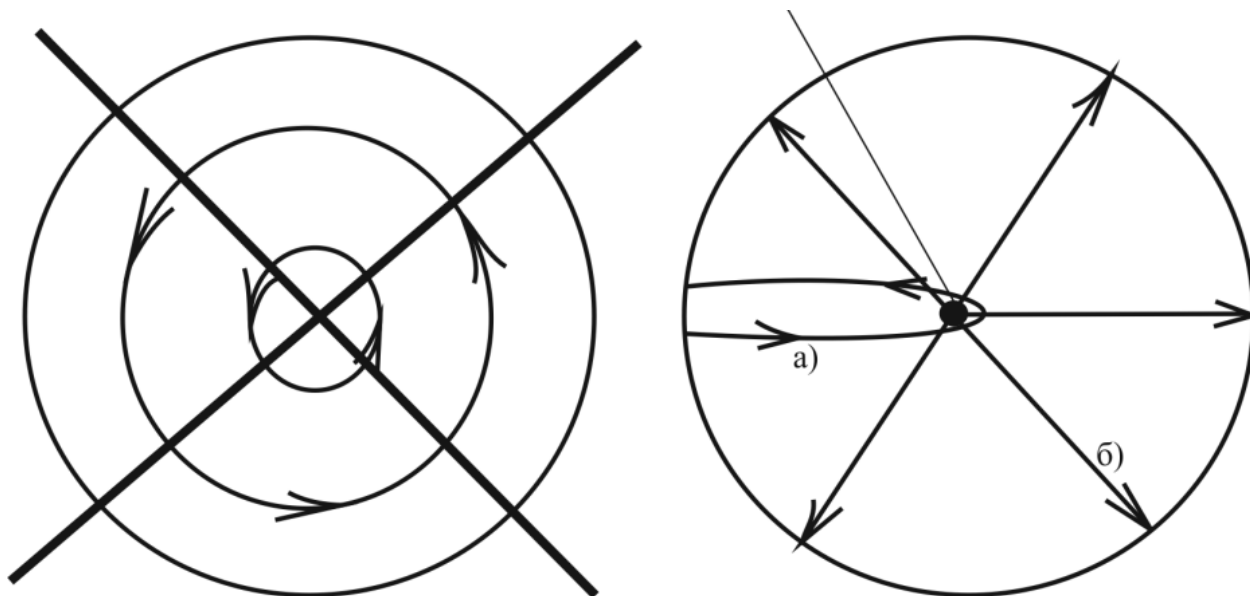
Направление движения заготовки при шлифовании на рабочей поверхности планшайбы (слева на рисунке – движение заготовки недопустимо, т.к. выработка плоскости будет неравномерной; справа – рекомендуемые варианты движения заготовки)
